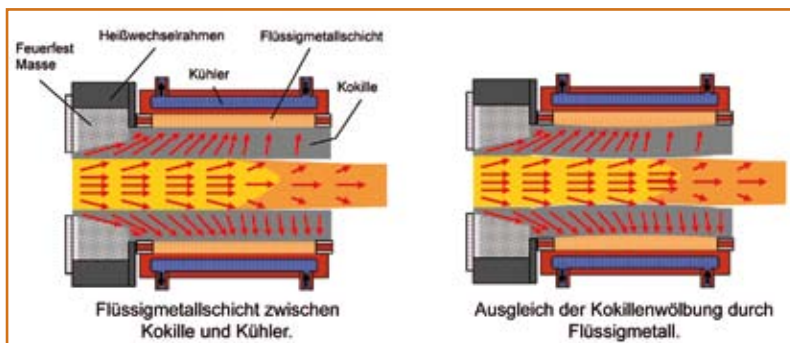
Kokillenaufbau mit Flüssigmetallschicht
